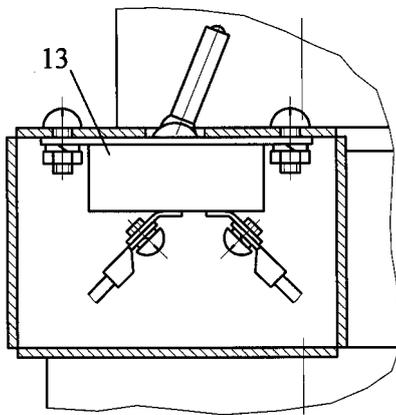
Питаящая установка для аварийного складывания
